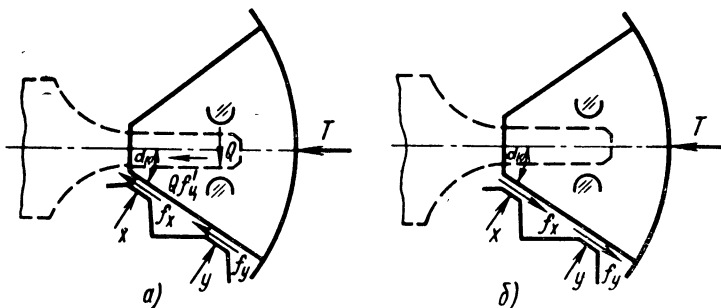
Схемы к расчету предварительного натяжения пружины и определения оптимального угла центрирующей конической поверхности α_k :
